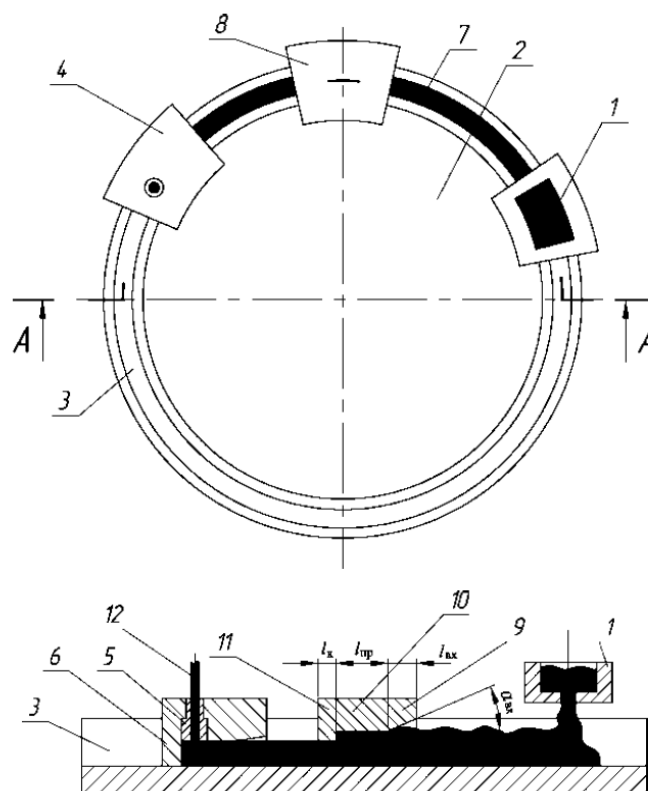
Схема установки непрерывного литья и прессования:
